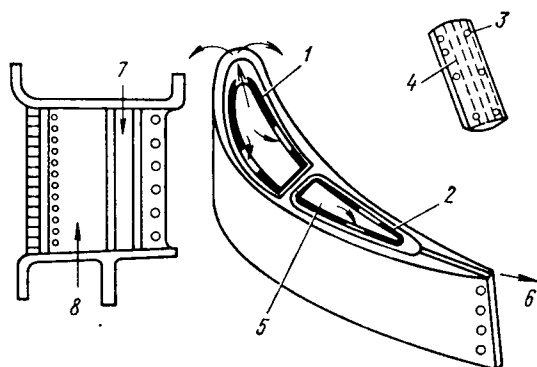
Сопловая лопатка первой ступени двигателя TF-39
